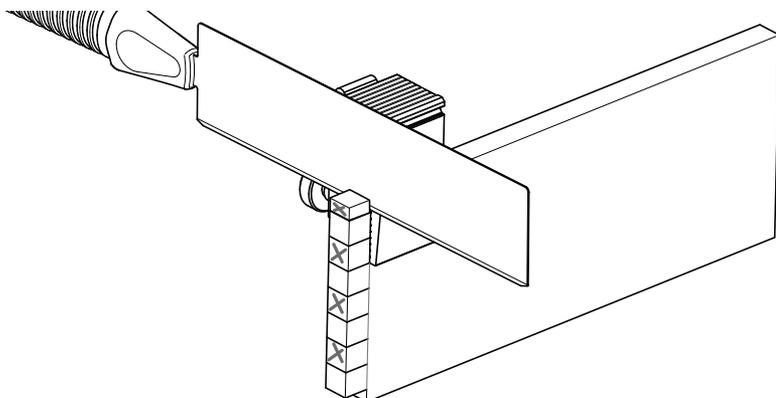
Tailler le rebut à l'extrémité d'une planche
